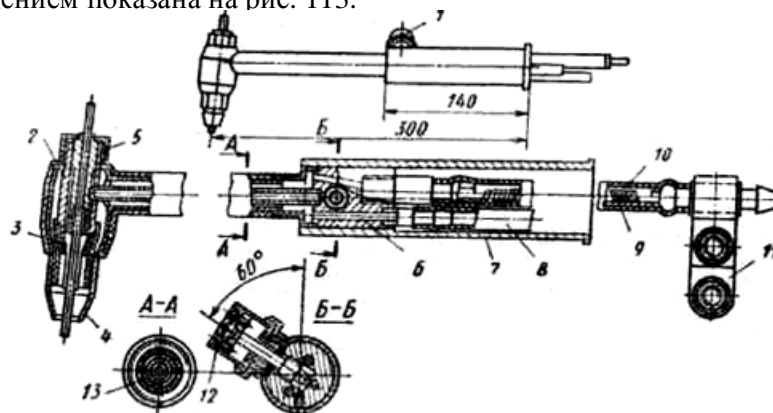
Схема установки для аргоно-дуговой электрической сварки неплавящимся вольфрамовым электродом на переменном токе: 1 — сварочный трансформатор; 2 — индуктивный регулятор сварочного тока; 3 — цанга для закрепления электрода; 4 — сопло; 5 — гайки; 6 — корпус горелки; 7 и 12 — изолирующие оболочки горелки; 8 и 10 — резиновый рукав для воды; 9 — сварочный провод, охлаждаемый водой; 11 — скоба для присоединения сварочного провода; 13 — ребра, разделяющие трубу на две части при подводе холодной воды и отводе горячей воды
